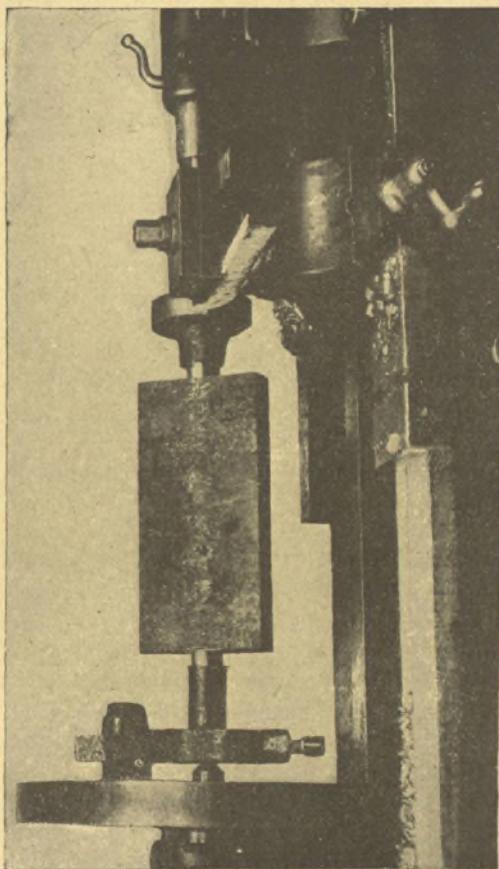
Dégrossissage d'un plateau d'acier forgé destiné à la fabrication d'un arbre manivelle à quatre coudes (montage entre pointes). Ce plateau rectangulaire sera ensuite découpé à la scie pour dessiner les manivelles et les manetons, puis usiné entièrement sur le tour par montage sur cales excentriques.
